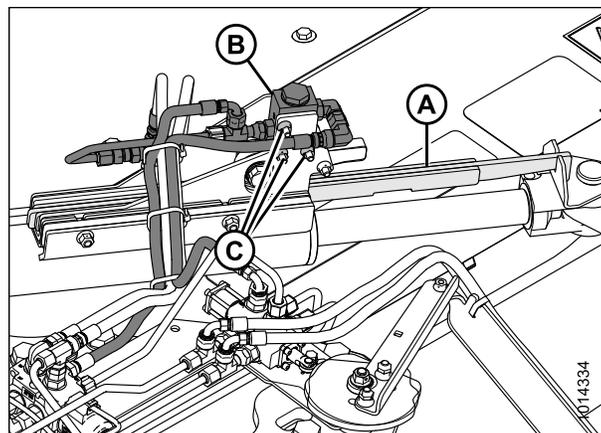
Contrôle d'alignement (vue de l'arrière, à droite)
